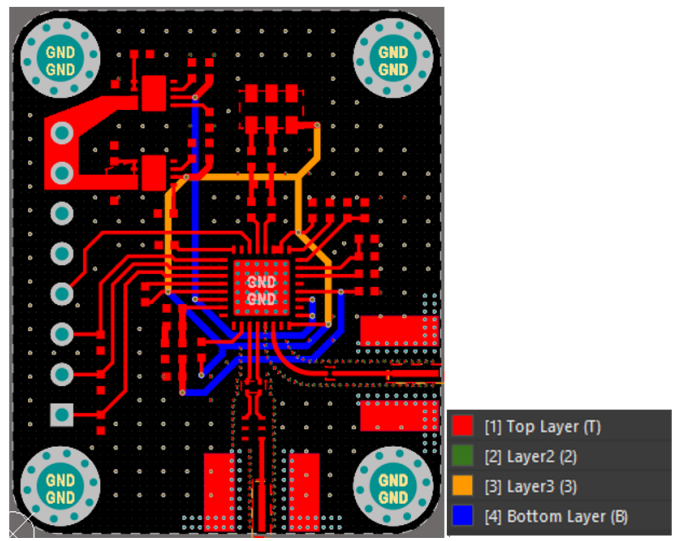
鎖相迴路振盪電路之 PCB 線路佈局圖
